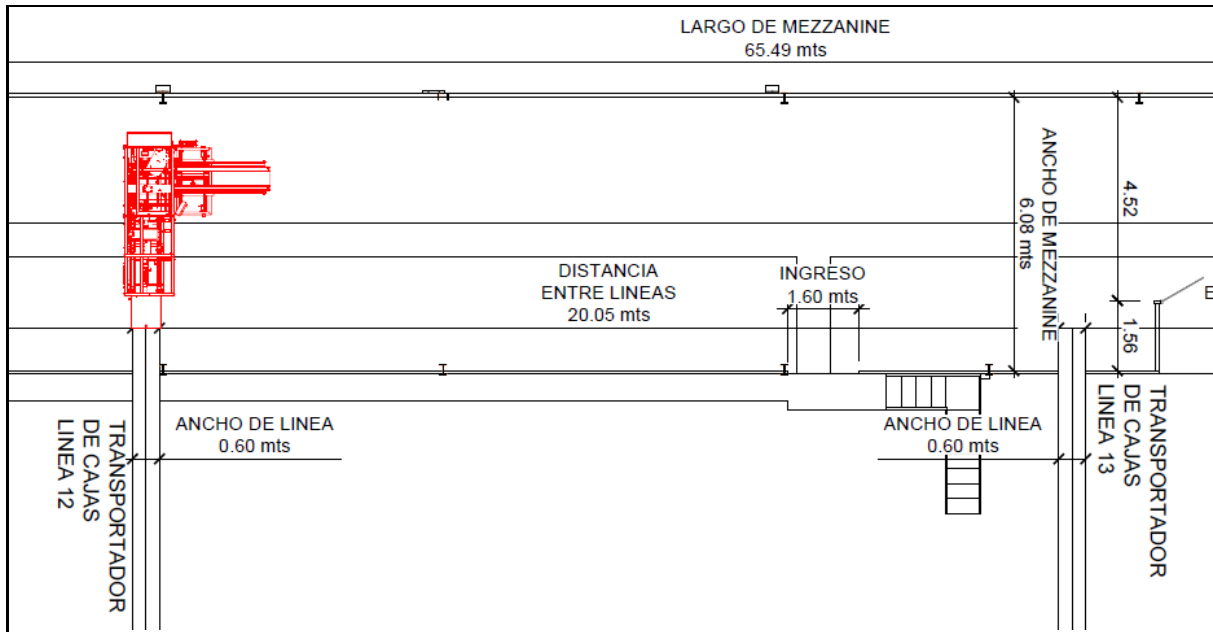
Armadora de caja situada en línea de producción M12 en planos AutoCAD
